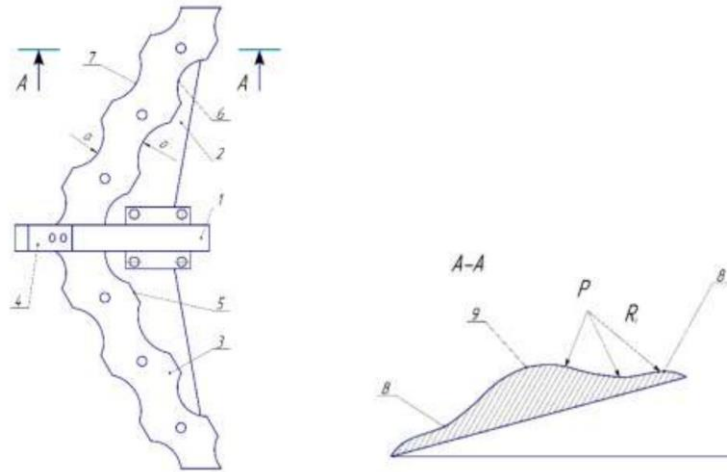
Робочі органи із зубчастими або хвилястими формами робочих поверхонь [17].
